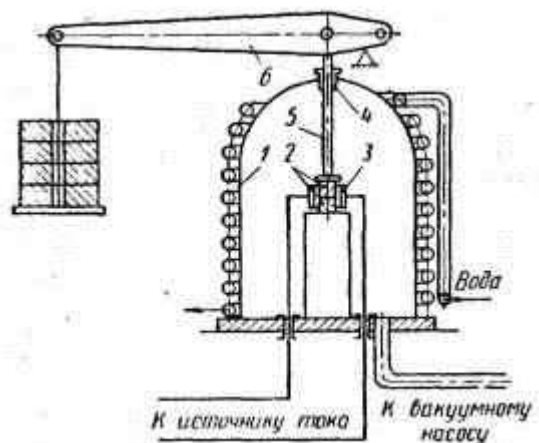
Схема установки для диффузионной сварки в вакууме
